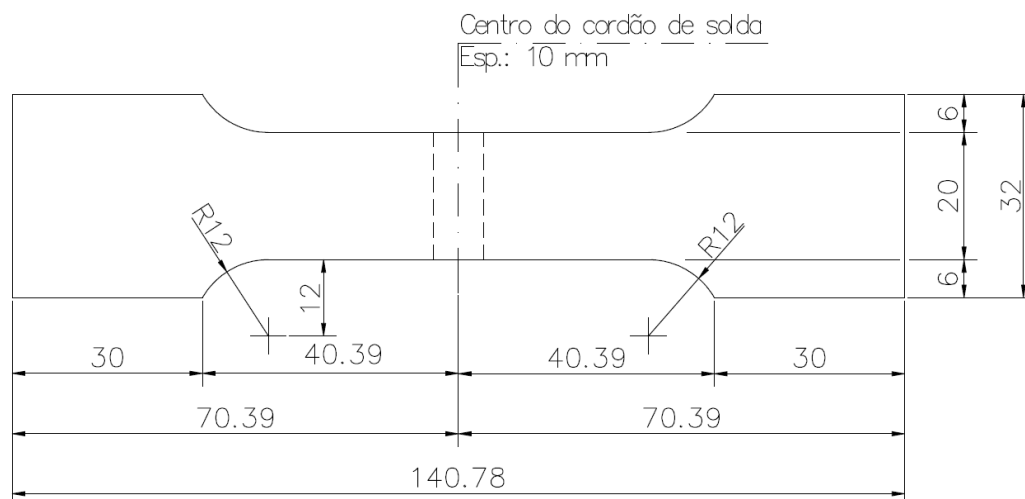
Dimensões do corpo-de-prova de tração na junta.
